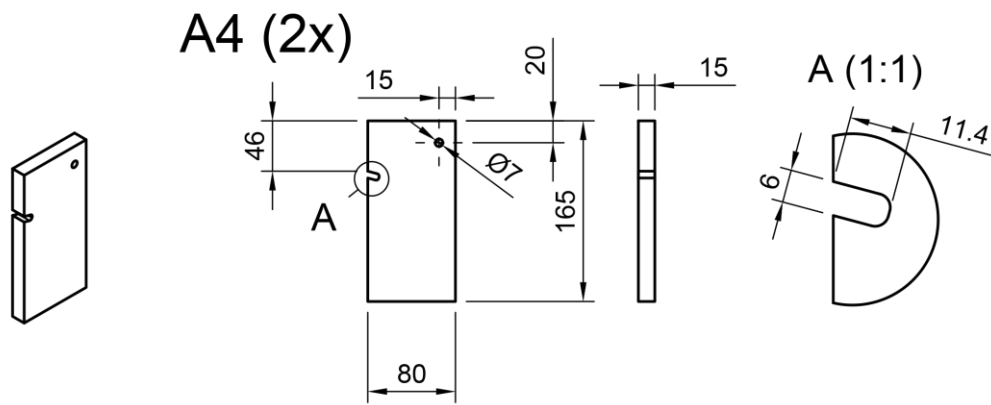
Ускоритель частиц – Детализированный вид - 3
